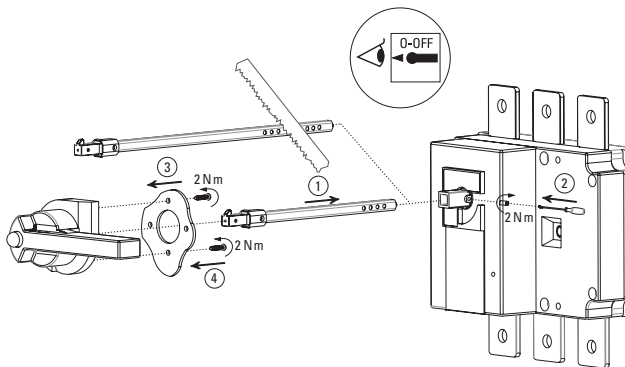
а – Порядок монтажа выносной ручки для рубильников 160-630 А
